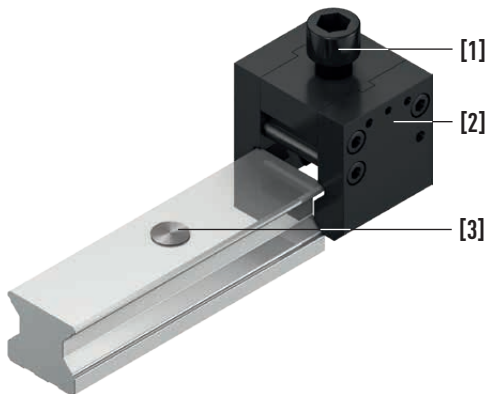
Positionieren des Montagewerkzeugs auf der Profilschiene
